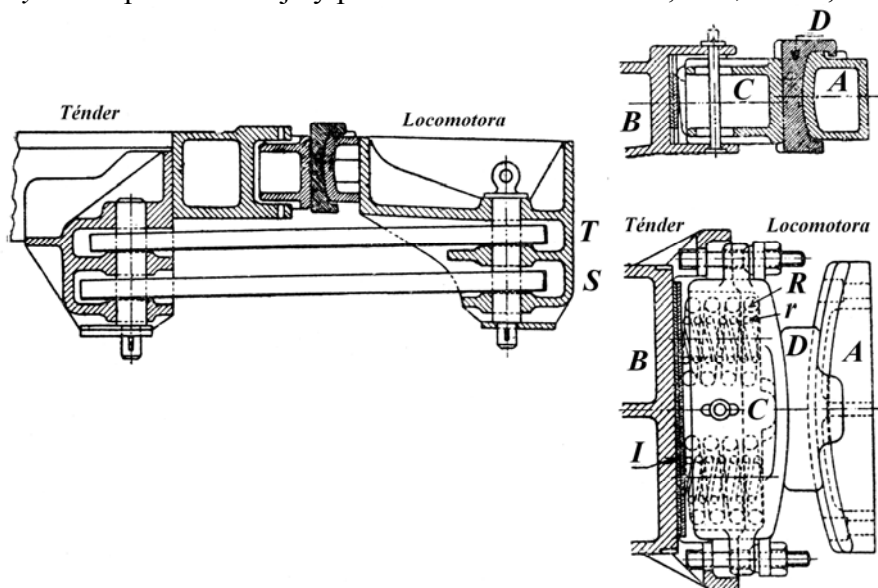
Enganche Franklin de las locomotoras americanas.
